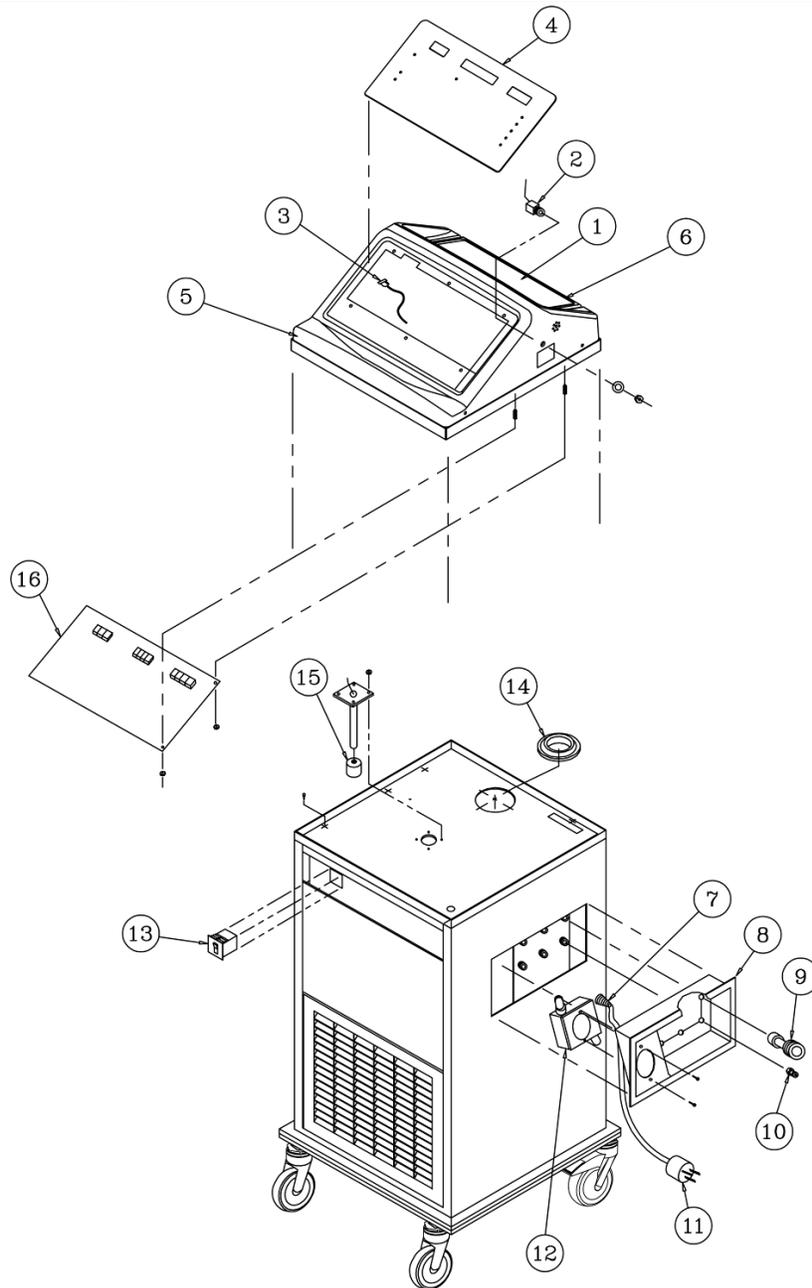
BLANKETROL III - DESGLOSE INTERNO - VISTA FRONTAL
